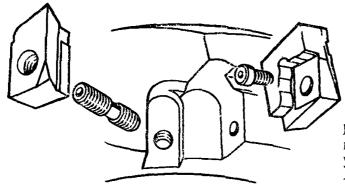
Пример унифицированного конструктивного решения установки съемного гиезда для закрепления пластины в модульной фрезе
